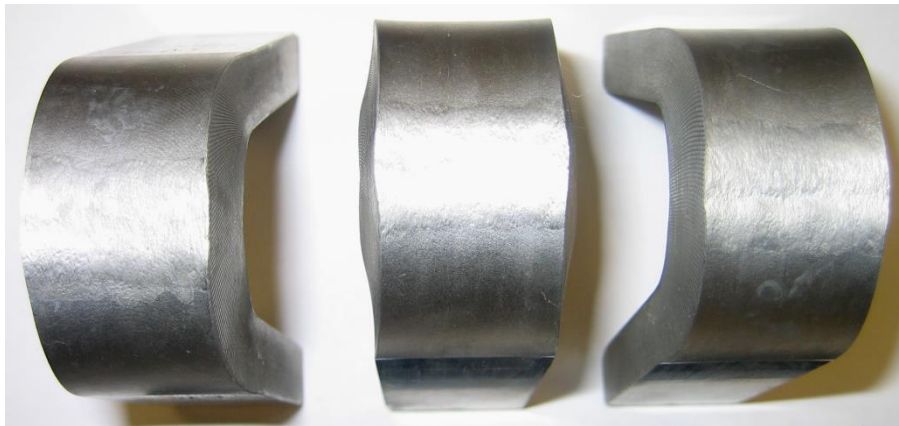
Образцы на загиб сварного соединения
